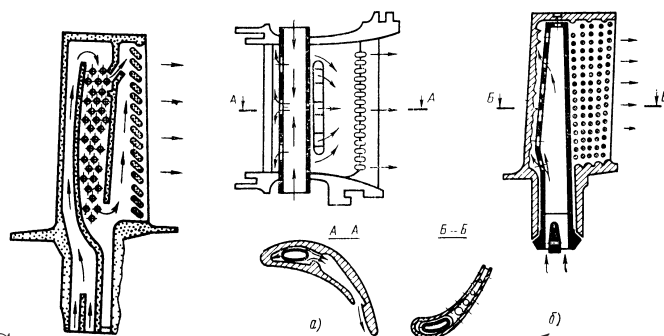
Слева - конструктивная схема рабочей лопатки со смешанным продольно-поперечным направлением движения охлаждающего воздуха и петлевым движением в продольном направлении (вторая ступень двигателя JT9D); справа - конструктивные схемы турбинных лопаток с дефлекторными вставками (а - сопловая лопатка первой ступени турбины двигателя «Конкуэй»; б - рабочая первой ступени - JT9D-7)
